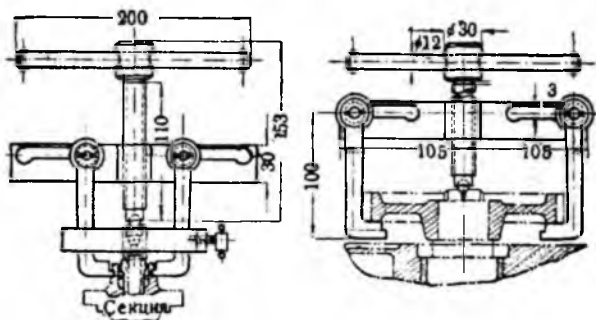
Съемник для спрессовки шестерни кулачкового вала и стопорного кольца секции насоса ЧТЗ.
